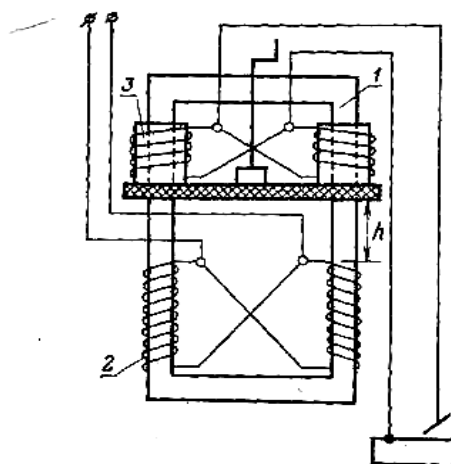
Схема сварочного трансформатора ТД-300:
